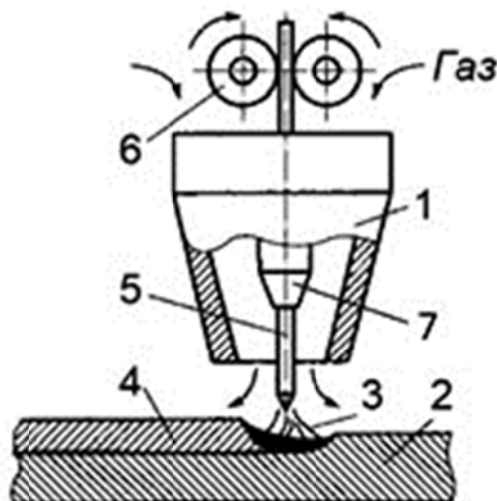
Схема дуговой сварки в среде защитных газов плавящимися электродами:
